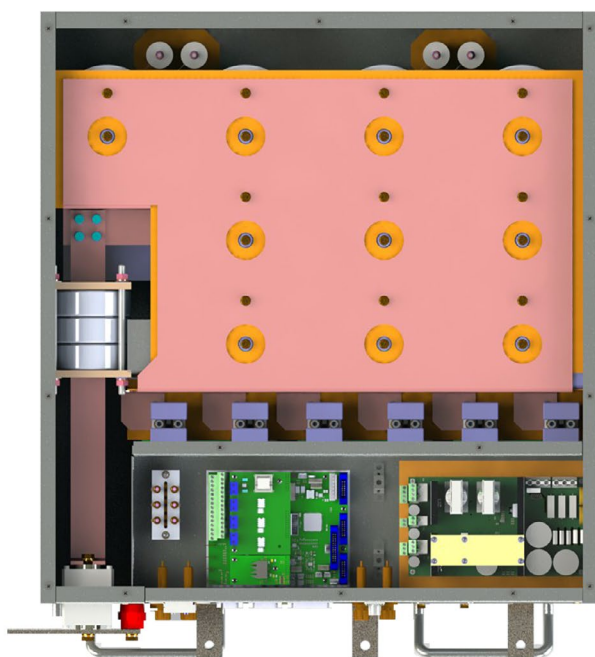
Внешний вид системы управления ячейки инвертора
